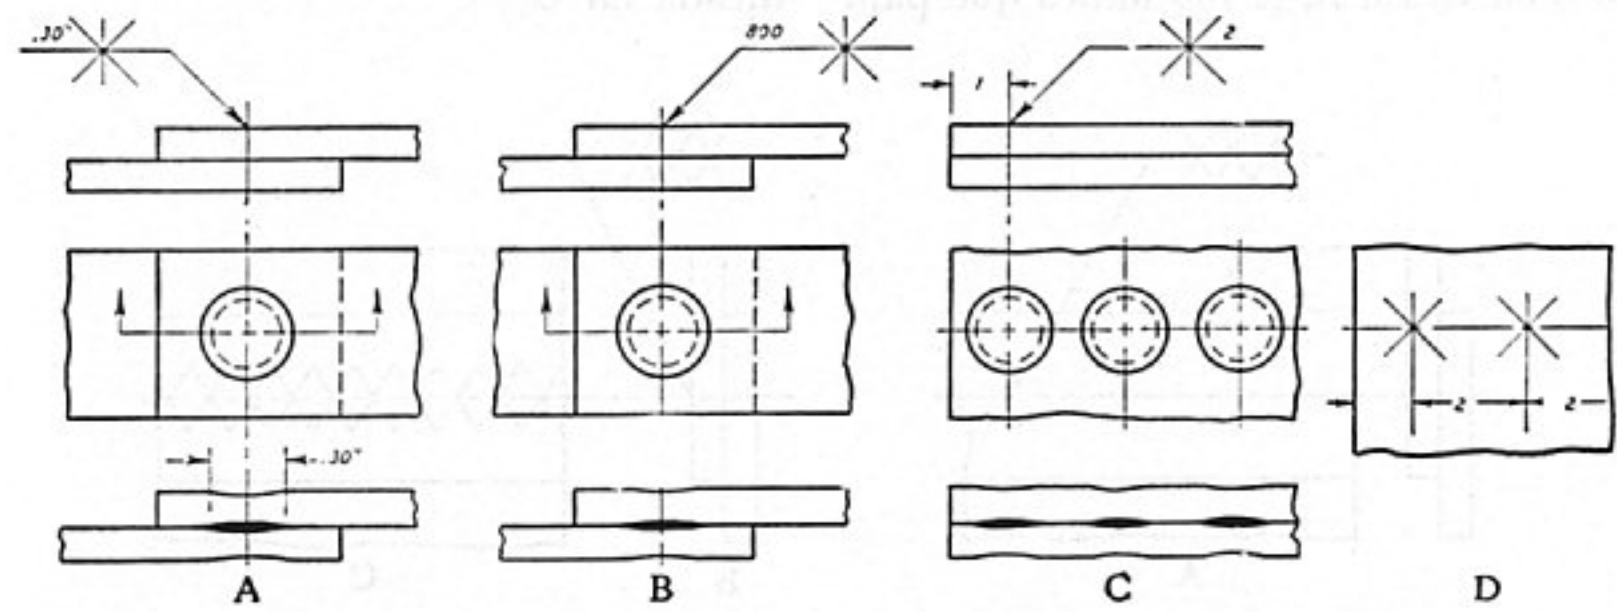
Símbolos de soldadura por puntos.
